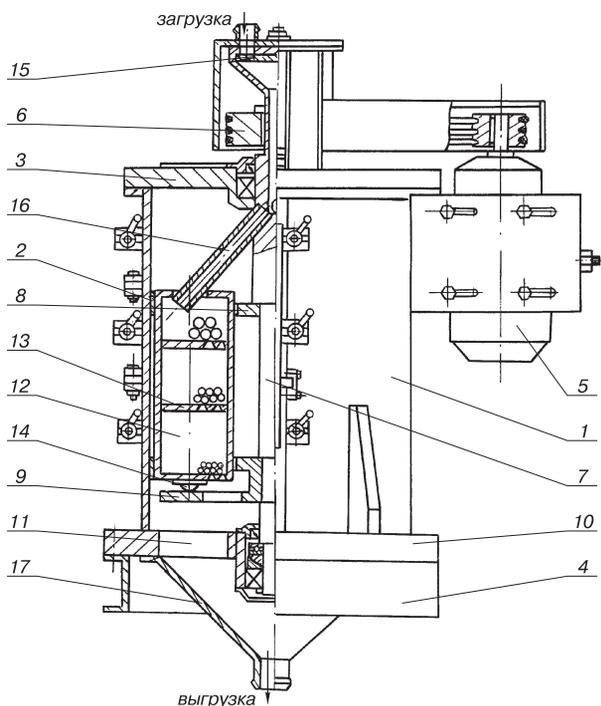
Мельница планетарная: 1 – корпус; 2 – кольцо беговое; 3 – крышка; 4 – рама; 5 – электродвигатель; 6 – передача клиноремennая; 7 – вал; 8, 9 – водила; 10 – нижняя плита корпуса; 11 – разгрузочные окна; 12 – барабан рабочий; 13 – решетка; 14 – опора шаровая; 15 – устройство загрузочное; 16 – патрубок; 17 – воронка разгрузочная
